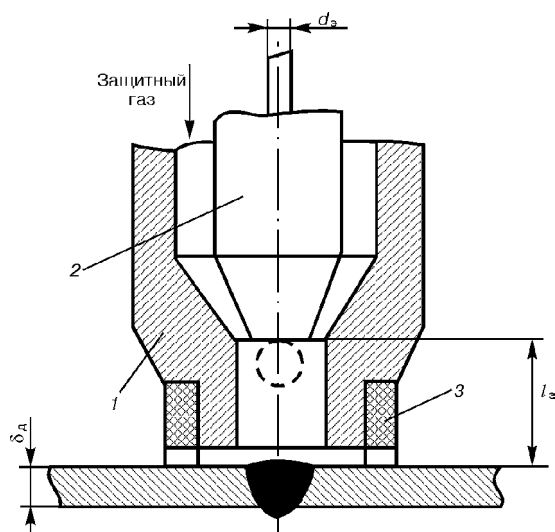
Схема процесса дуговой точечной сварки: 1 — сопло; 2 — теплоотводящий мундштук; 3 — опорная втулка
